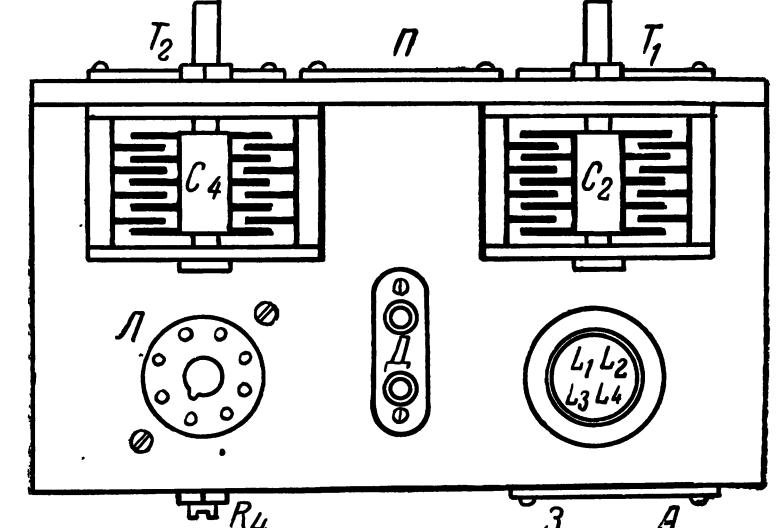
Расположение деталей на угловой панели однолампового приёмника (вид сверху).
